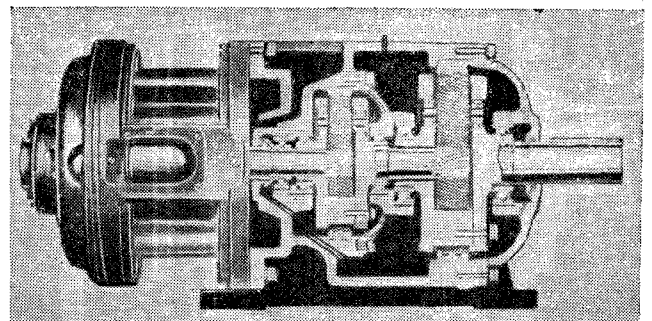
Редукторный двигатель фирмы GEC с двойной передачей на 63,5—13 об/мин (разрез)
